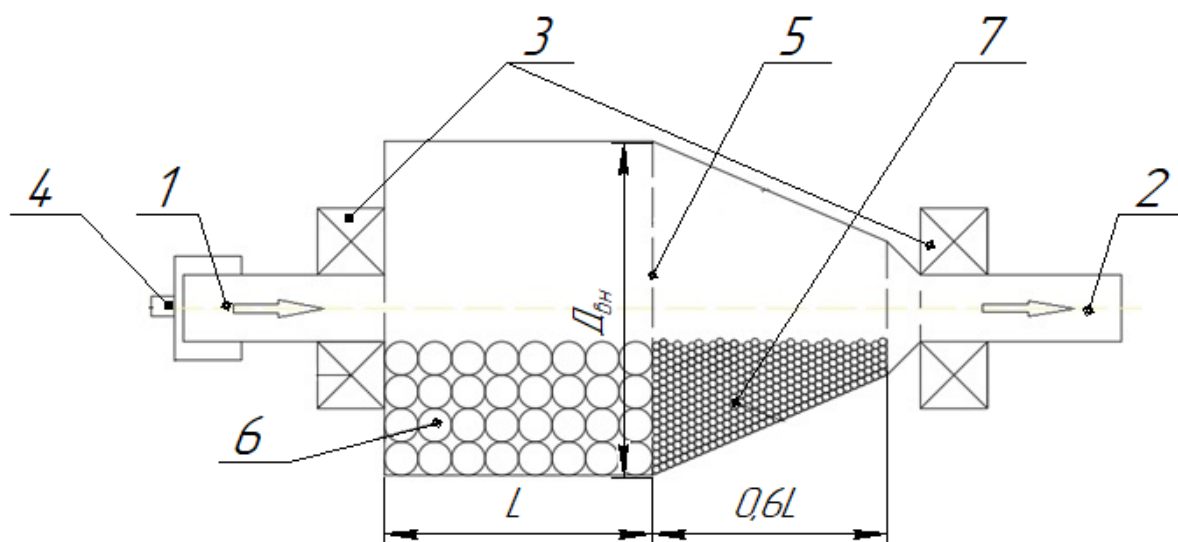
Конструкция шаровой мельницы: 1 – впускающий патрубок; 2 – выпускающий патрубок; 3 – подшипники качения; 4 – жиклер; 5 – решетка перфорированная; 6 – шары большего диаметра; 7 – шары меньшего диаметра
